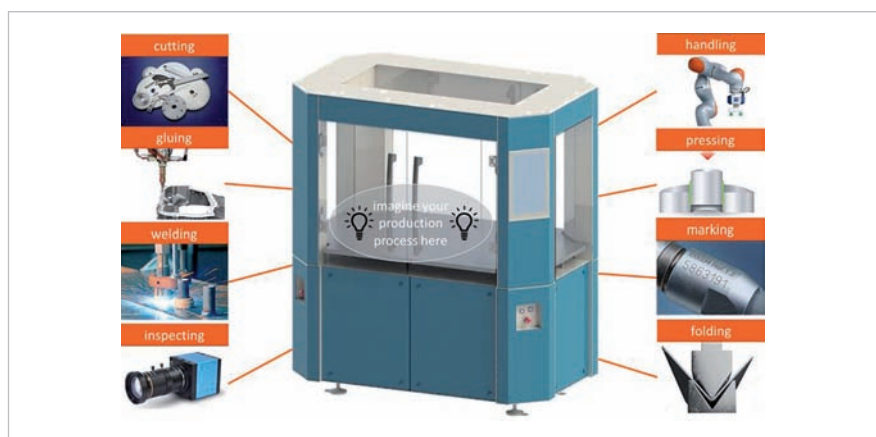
Koncept projektu RoboWeldAR (vlastníctvo DIH²)
